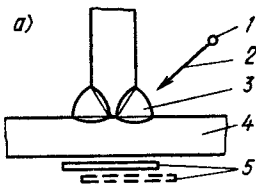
Схемы испытания швов тавровых сварных соединений (обозначения те же, что и на рис. 11.13)
